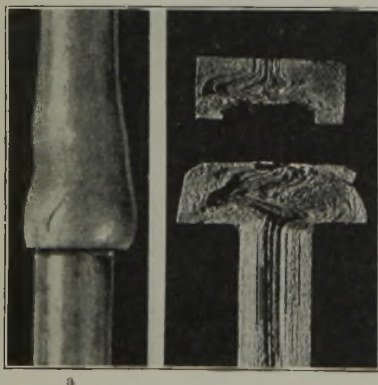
Ausknicken des Drahtes infolge Seigerung. a = Vorstauch eingeknickt; b = Schrauben; c = abgerissener Kopf.
